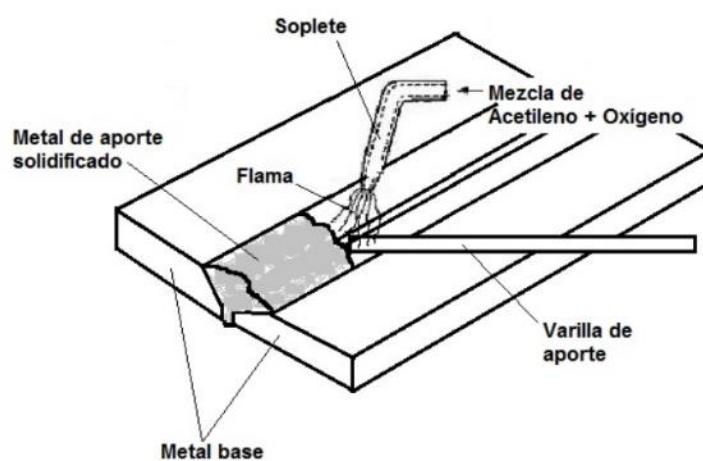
Proceso de la soldadura fuerte y blanda.
